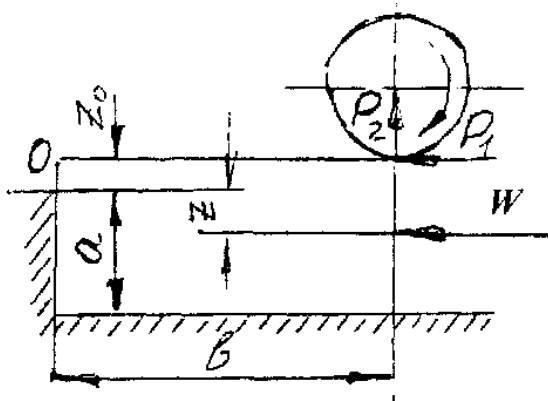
Затиск заготовки бічною силою при фрезеруванні
